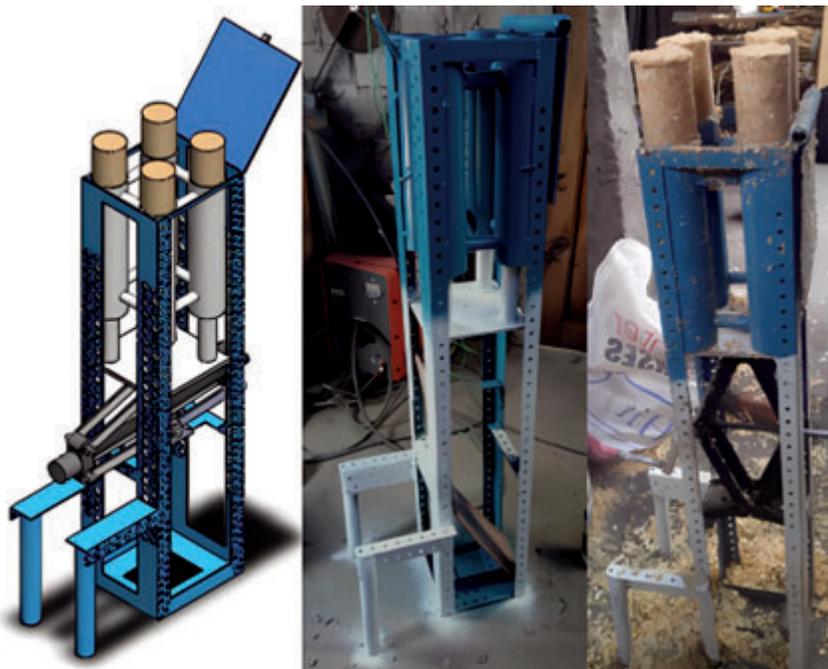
a) diseño terminado, b) construcción física, c) máquina en operación.
